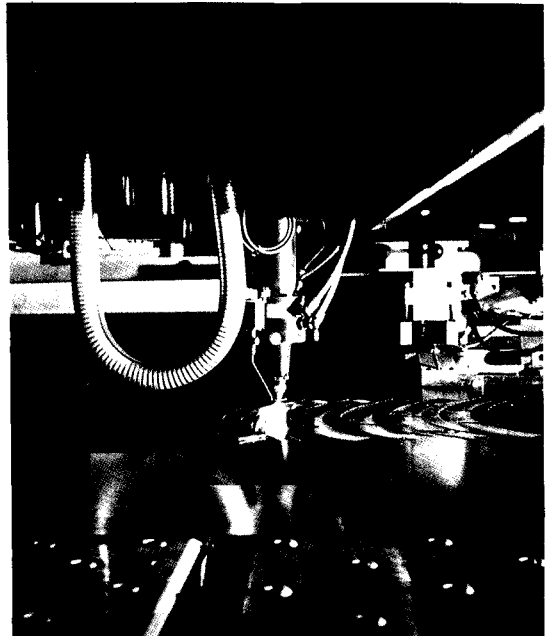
난삭재에 대한 Blade형상의 NC LASER cutting 가공례
